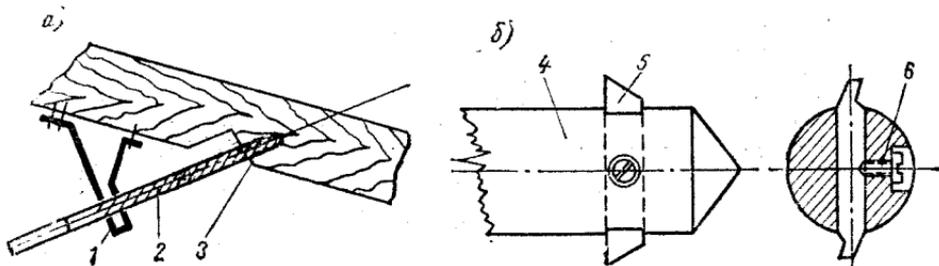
Приспособления для сверления отверстия под дейдвудную трубу: а — кронштейн-кондуктор; б — расточка.
